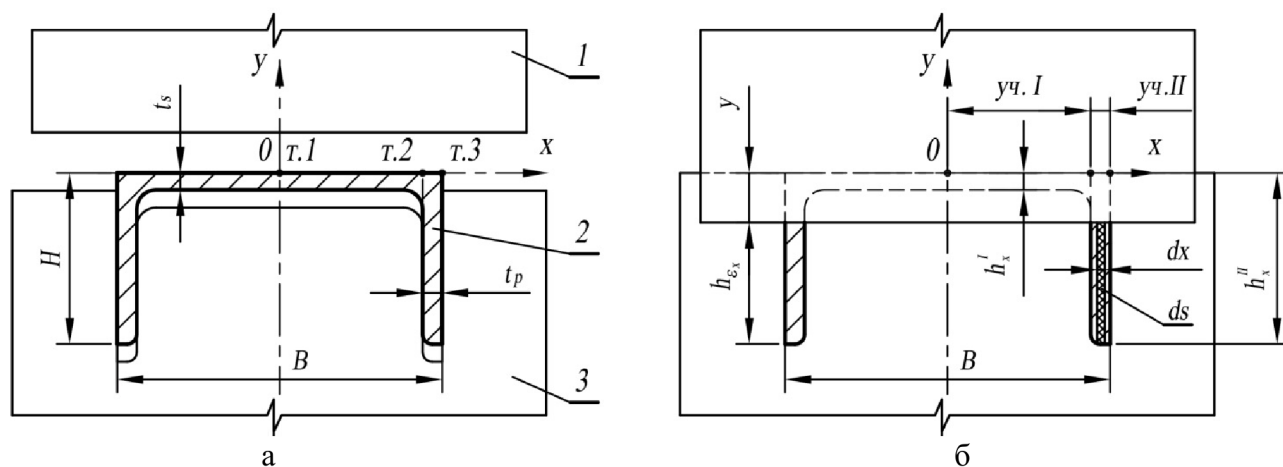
Схема к определению силы резки швеллера фасонными ножами; а – расположение ножей и заготовки до начала резки; б – в процессе резки
